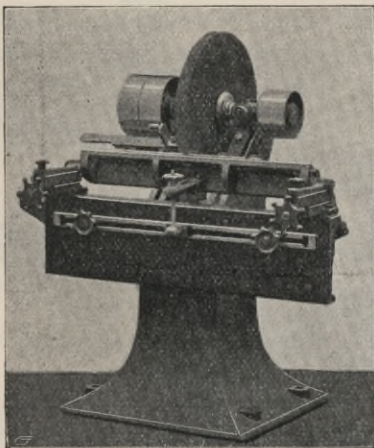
Selbsttätige Hobelmesserschleifmaschine.
